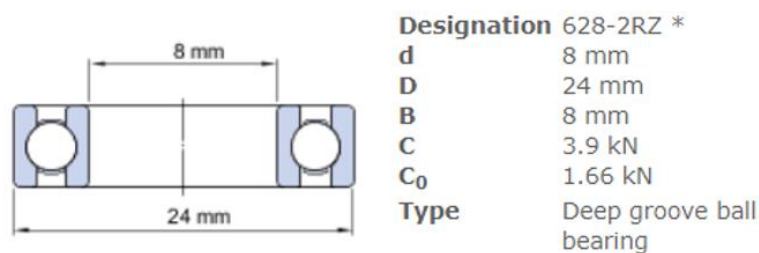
Características de rodamiento de bolas 628-2RZ. Fuente: <http://webtools3.skf.com/BearingCalc/>
